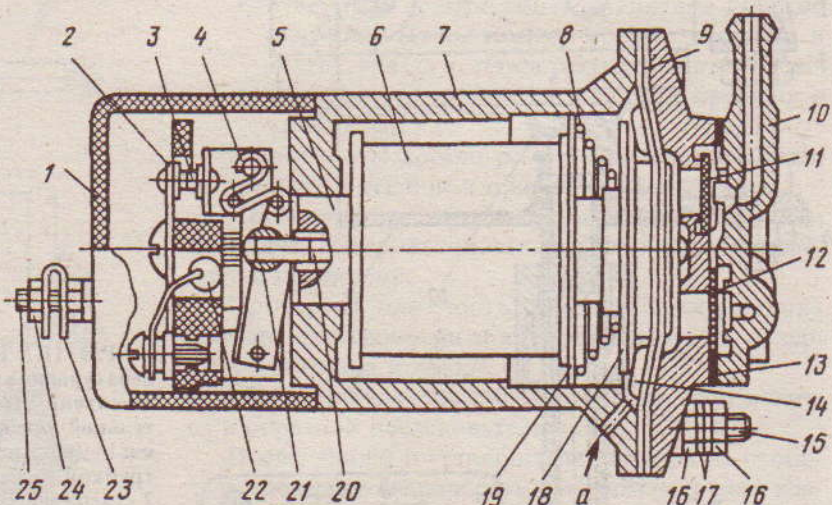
Электромагнитный бензонасос: 1 - крышка; 2 - неподвижный контакт с пластиной в сборе; 3 - подвижный контакт с рычажным устройством в сборе; 4 - пружинное коромысло; 5 - сердечник электромагнита; 6 - катушка электромагнита; 7 - корпус; 8 - пружина; 9 - диафрагма; 10 - крышка с клапанами в сборе; 11 - нагнетательный клапан; 12 - всасывающий клапан; 13 - прокладка крышки; 14 - опорная немагнитная шайба; 15 - шпилька крепления провода "масса"; 16 - гайка; 17 - шайба; 18 - якорь; 19 - немагнитная шайба; 20 - шток; 21 - резьбовая бойка; 22 - резистор; 23 - клеммный зажим; 24 - гайка; 25 - клеммный болт; а - отверстие сообщения поддиафрагменной полости с атмосферой
